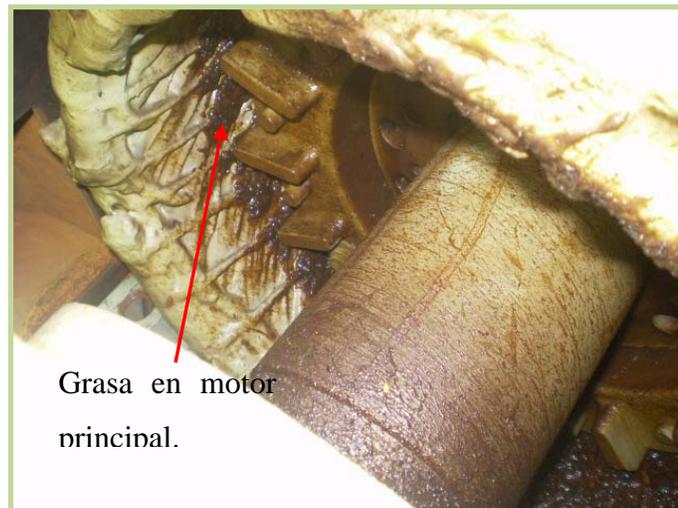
Rotor motor eléctrico principal del Top Drive.
